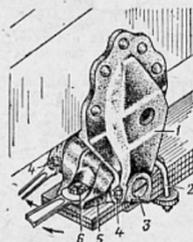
Подтяжка гайки болта ушка передней рессоры:
